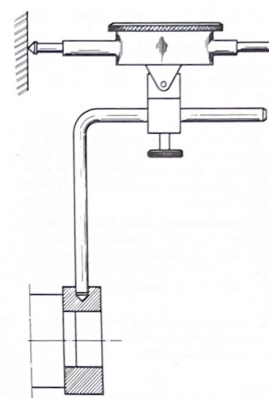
Esquema de montaje del comprobador sobre el soporte MR 3365-90 para comprobar los puntos de apoyo del cárter. La deformación máxima tolerada es de 0,1 mm.
